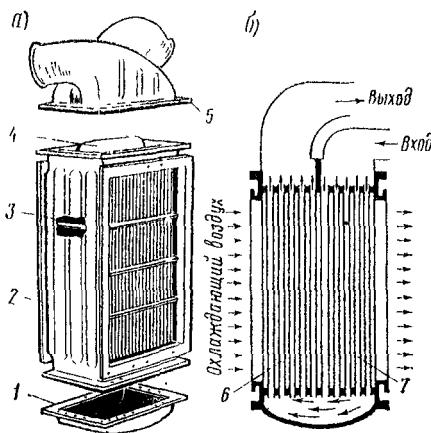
Радиатор воздухо-воздушный 1639А
